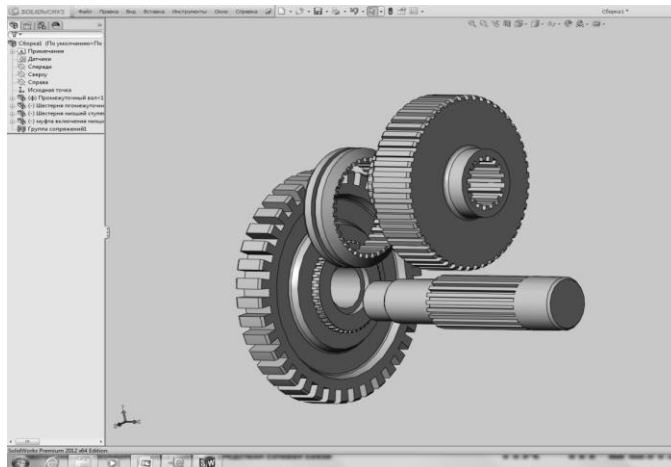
Сопряжение промежуточного вала, шестерни низшей ступени, муфты включения низшей ступени, шестерни промежуточного вала
